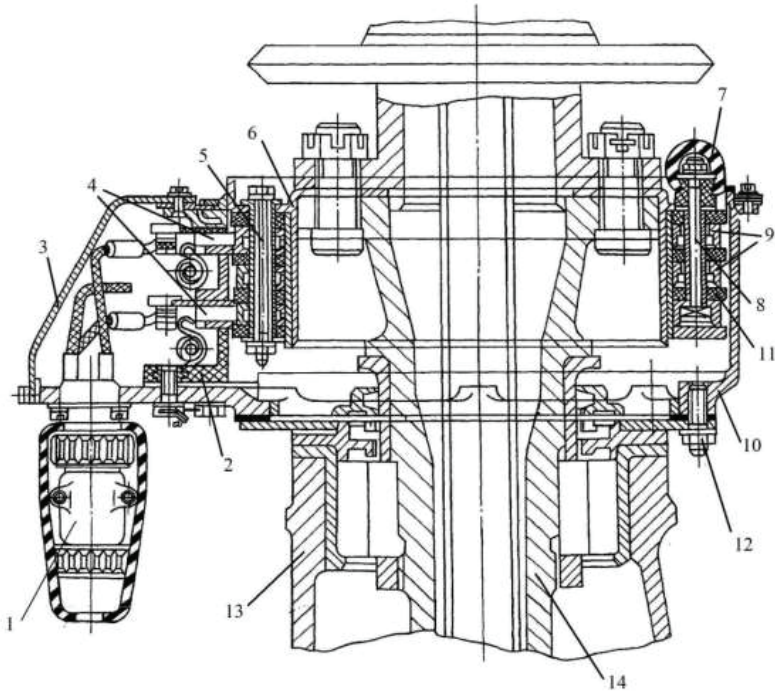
Токосъемник рулевого винта вертолета Ми-171, где 1 – штепсельный разъем; 2 – щеточная колодка; 3 – крышка; 4 – угольные щетки; 5 – стяжной болт; 6 – корпус; 7 – чехол; 8 – контактный болт; 9 – контактное кольцо; 10 – корпус щеткодержателя; 11 – изоляционное кольцо; 12 – стяжной болт; 13 – корпус хвостового редуктора (не вращающаяся часть); 14 – вал рулевого винта (вращающаяся часть)
